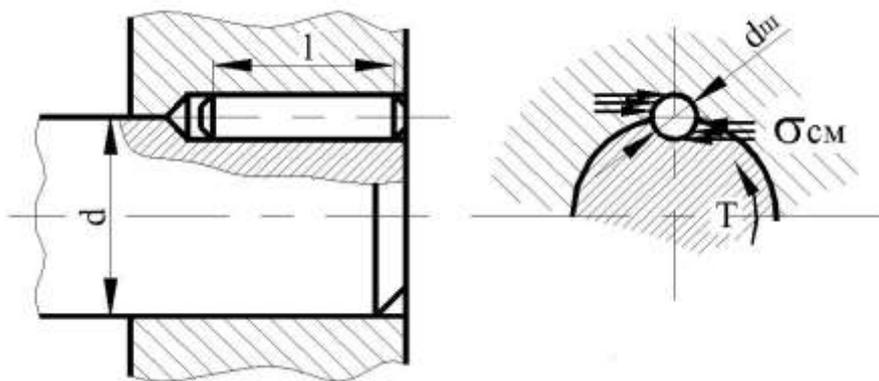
Розрахункова схема шпонкового з'єднання циліндричною шпонкою
